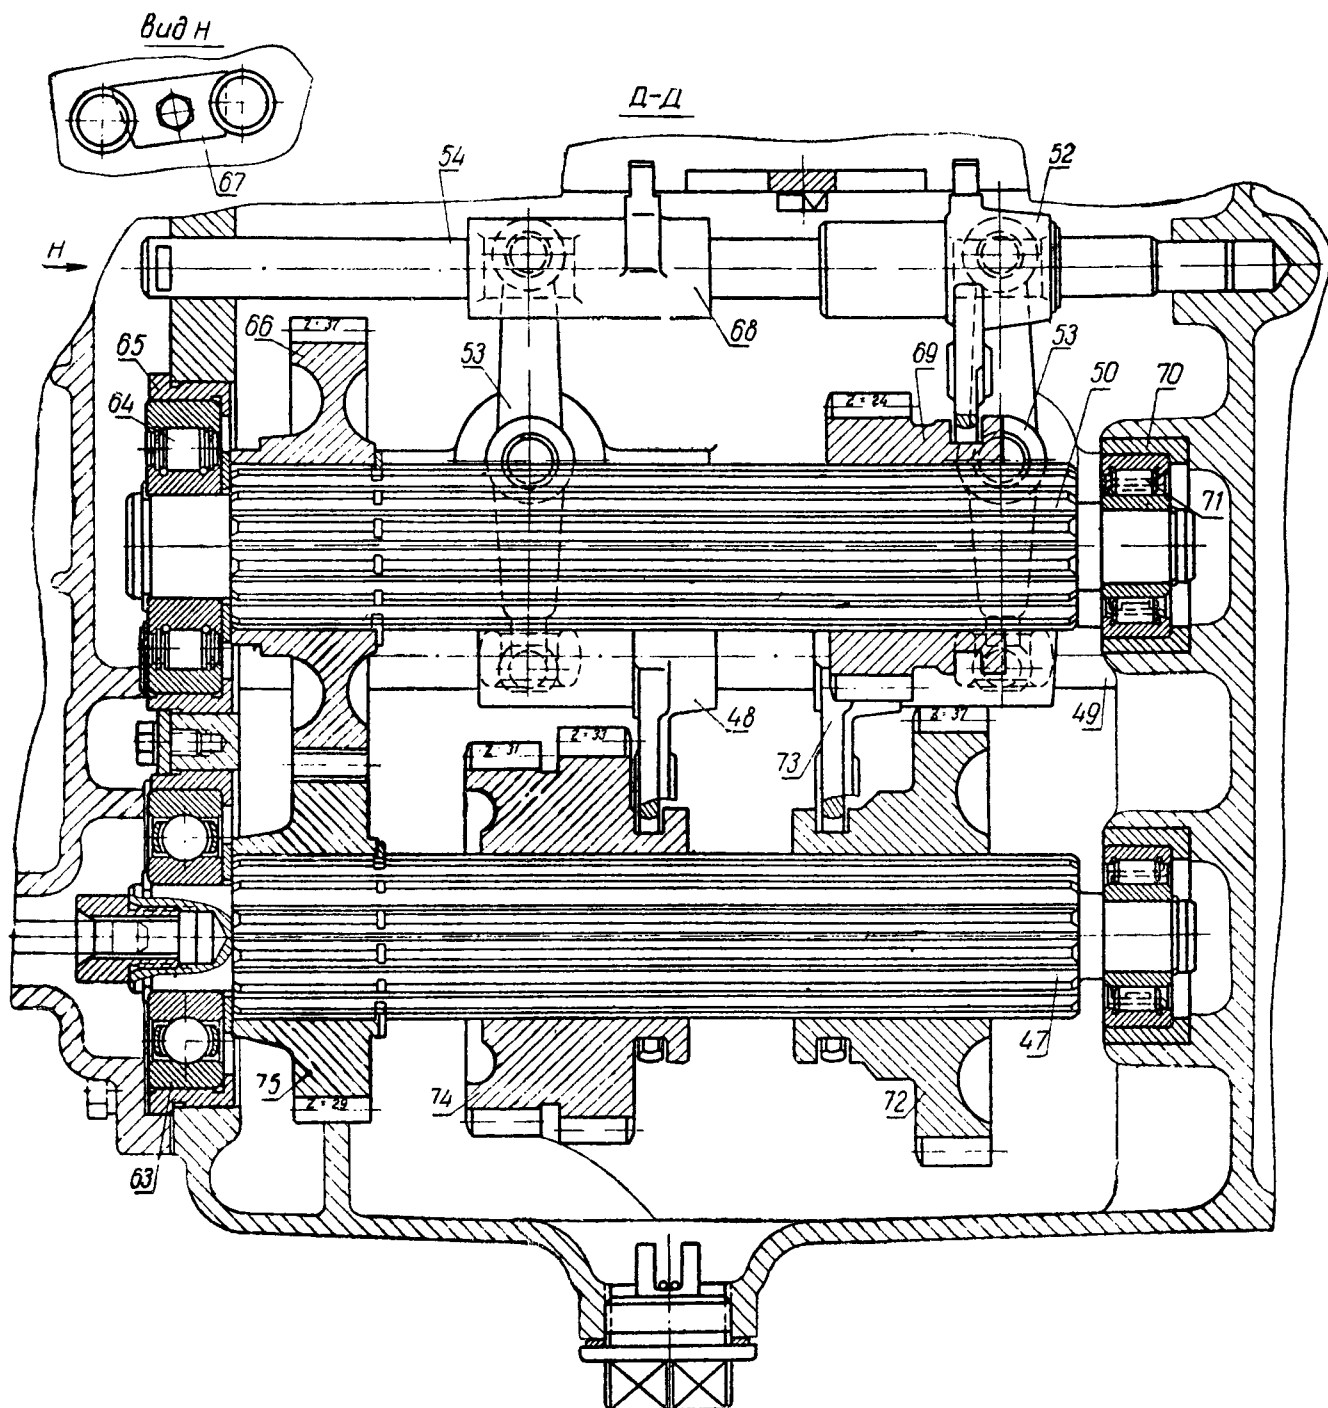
в. Коробка передач (разрез по валу заднего хода и дополнительному валу):
